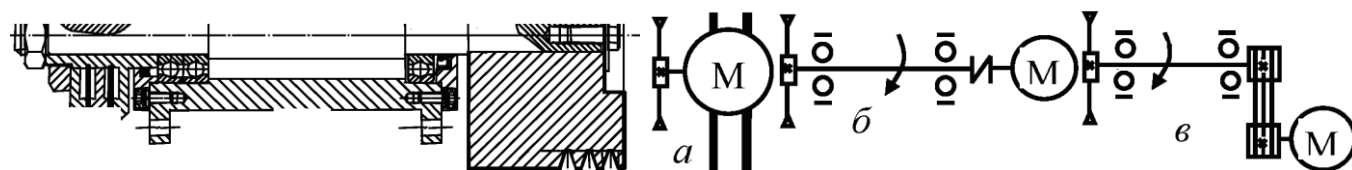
Способи з'єднання шпинделя з електродвигуном: *а* - як шпиндель використаний вал двигуна; *б* - муфтою; *в* - пасовою передачею
